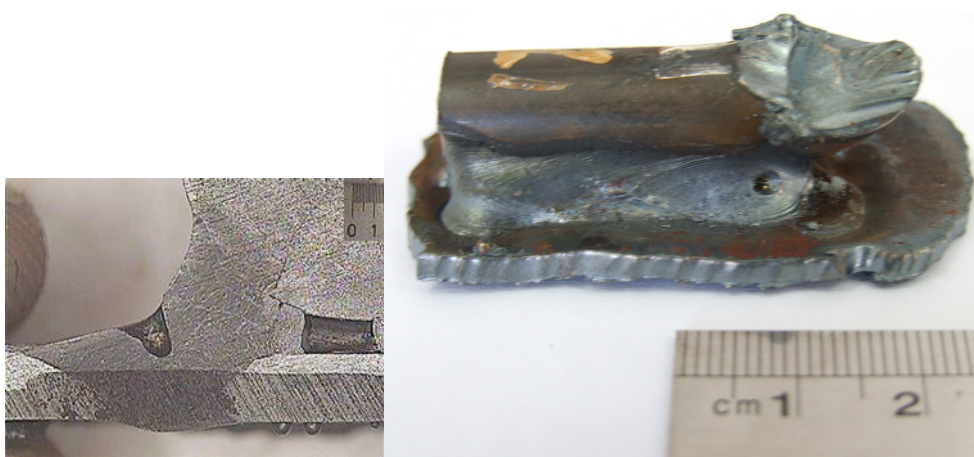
Porosidade na solda do gancho do quadro auxiliar
